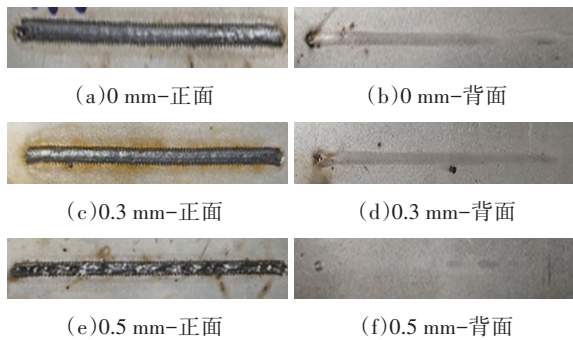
不同焊接摆幅下正面与背面的焊缝形貌
